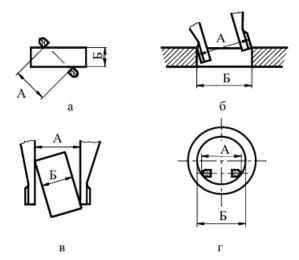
Примеры неправильной установки штангенциркуля: а, в -A > B; б, r - A < B
